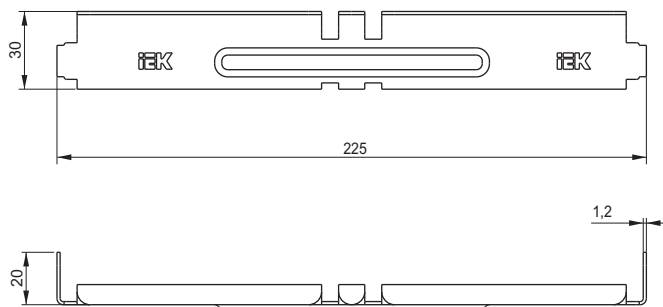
Соединитель безвинтовой / Figure B.1 – Screwless connector
